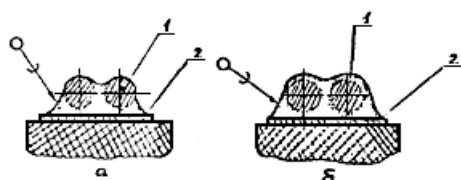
Соединение планарных выводов ИС с контактными площадками со смещением выводов
